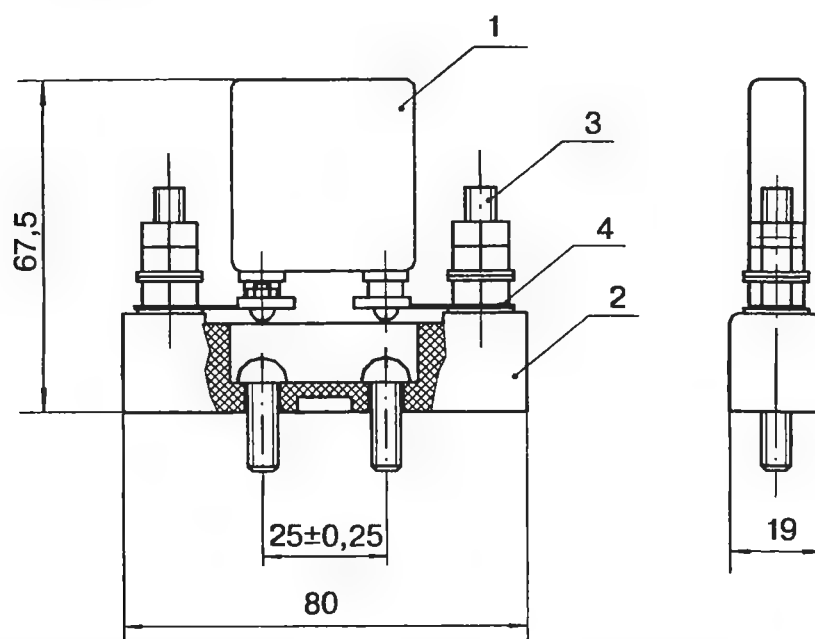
Внешний вид блока БЗП 1-10, где: 1 — варистор; 2 — контактная колодка; 3 — болт; 4 — контакт
